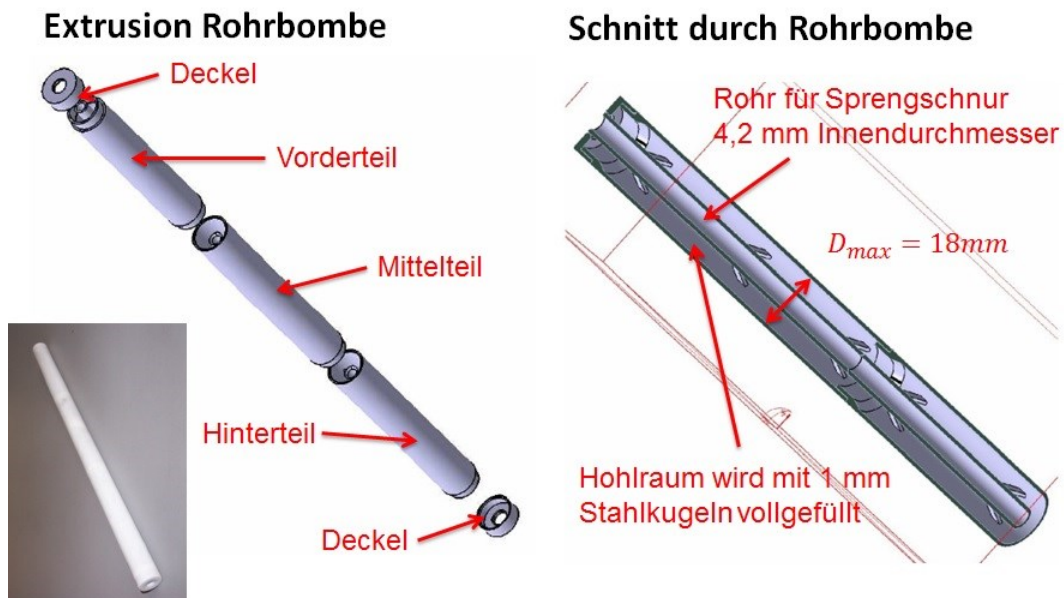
Extrusion der Einzelteile der Rohrbombe (links) und Schnitt durch die zusammengebauten Einzelteile (rechts)
